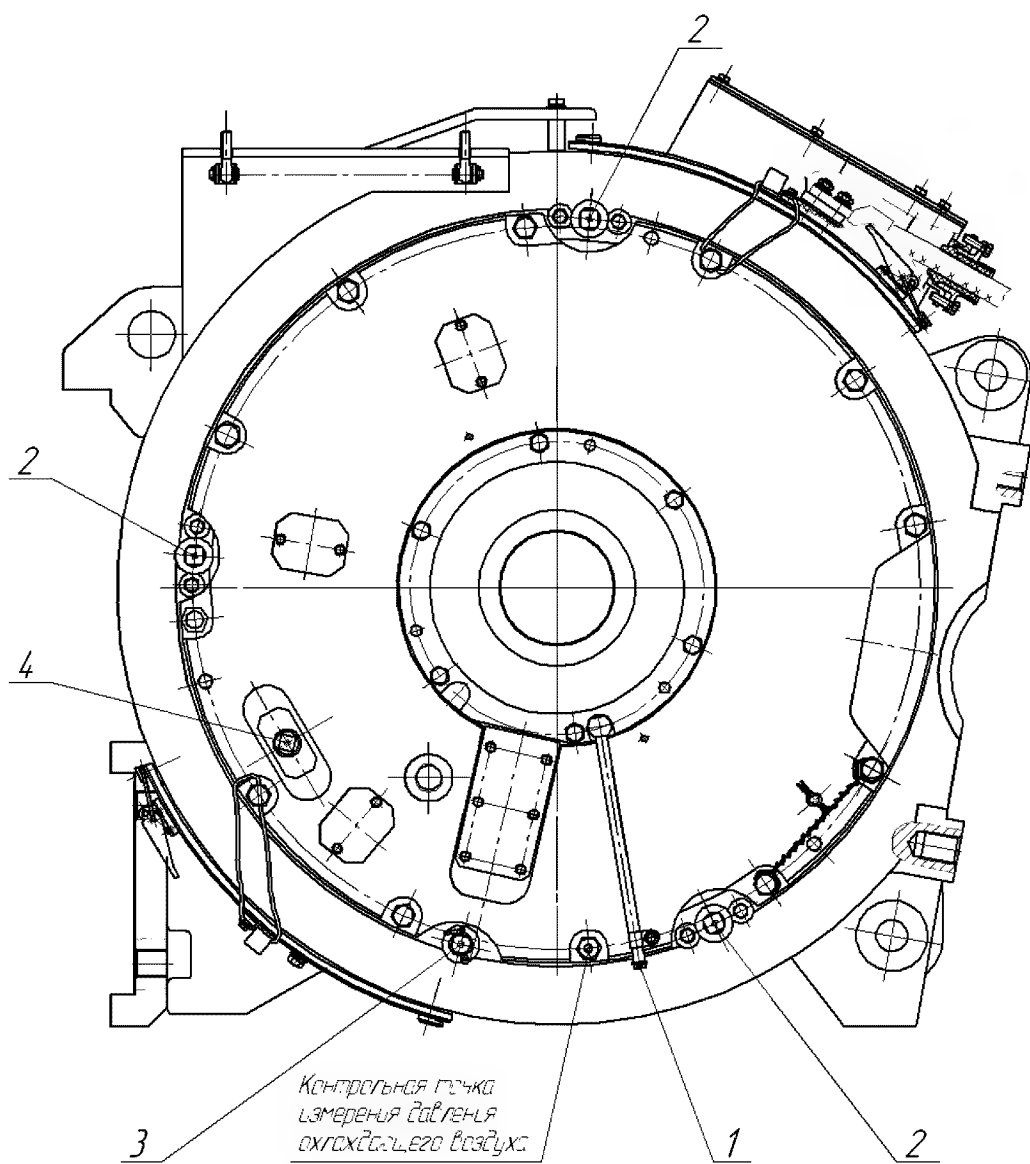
Вид на тяговый двигатель со стороны коллектора
